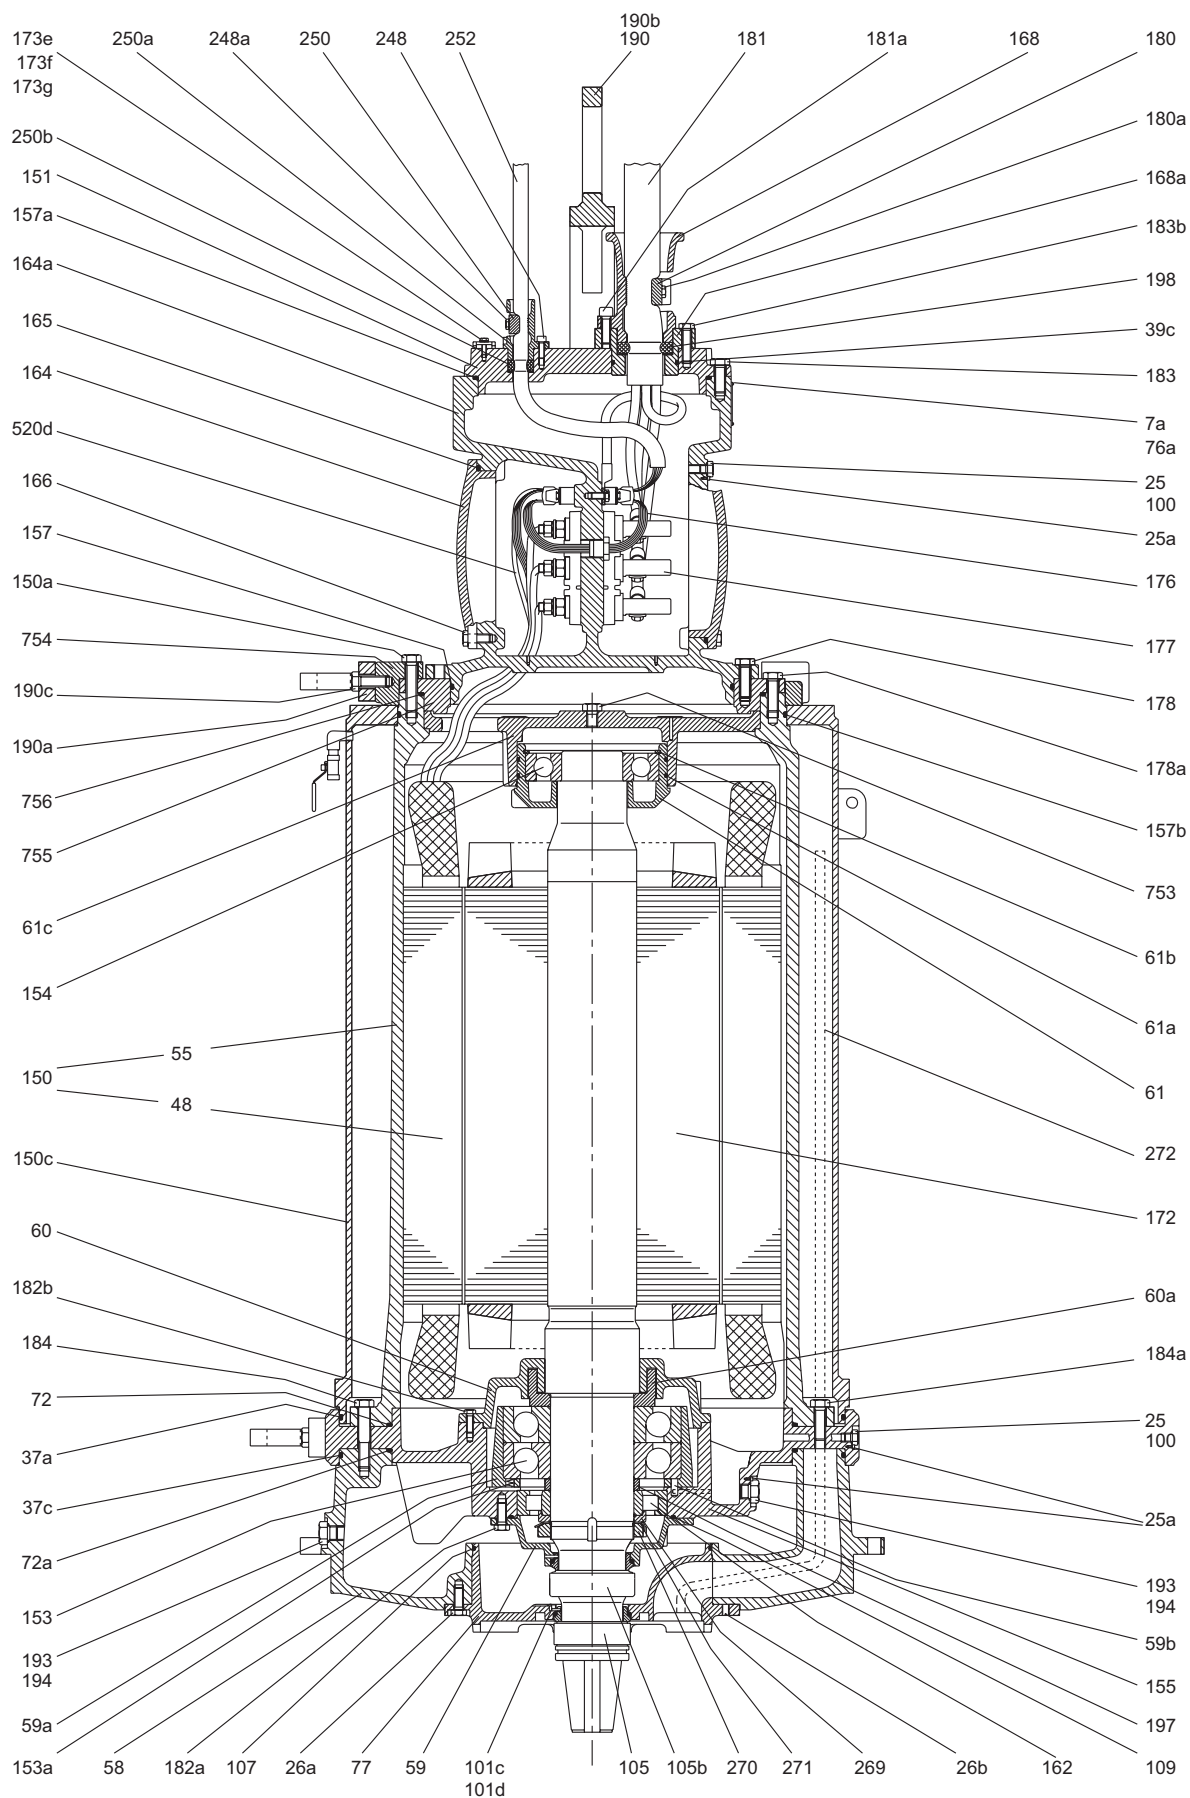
Типоразмер 78, невзрывозащищённый двигатель с охлаждающим кожухом.
